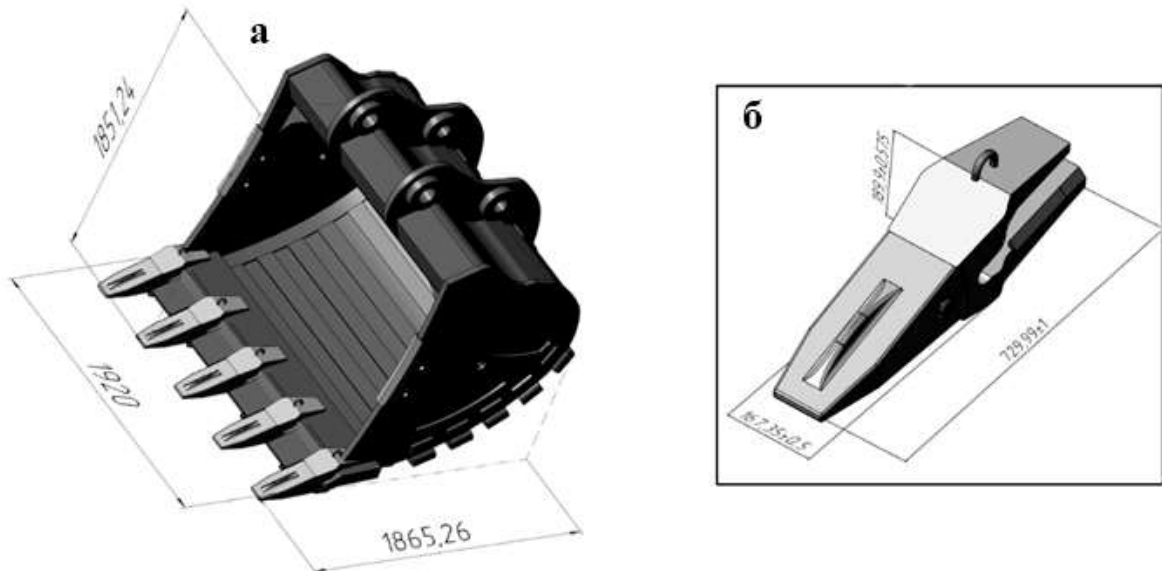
CAD-сборка ковша (а) и зуба в сборе (б) экскаватора Komatsu PC400LC-7 [96]
